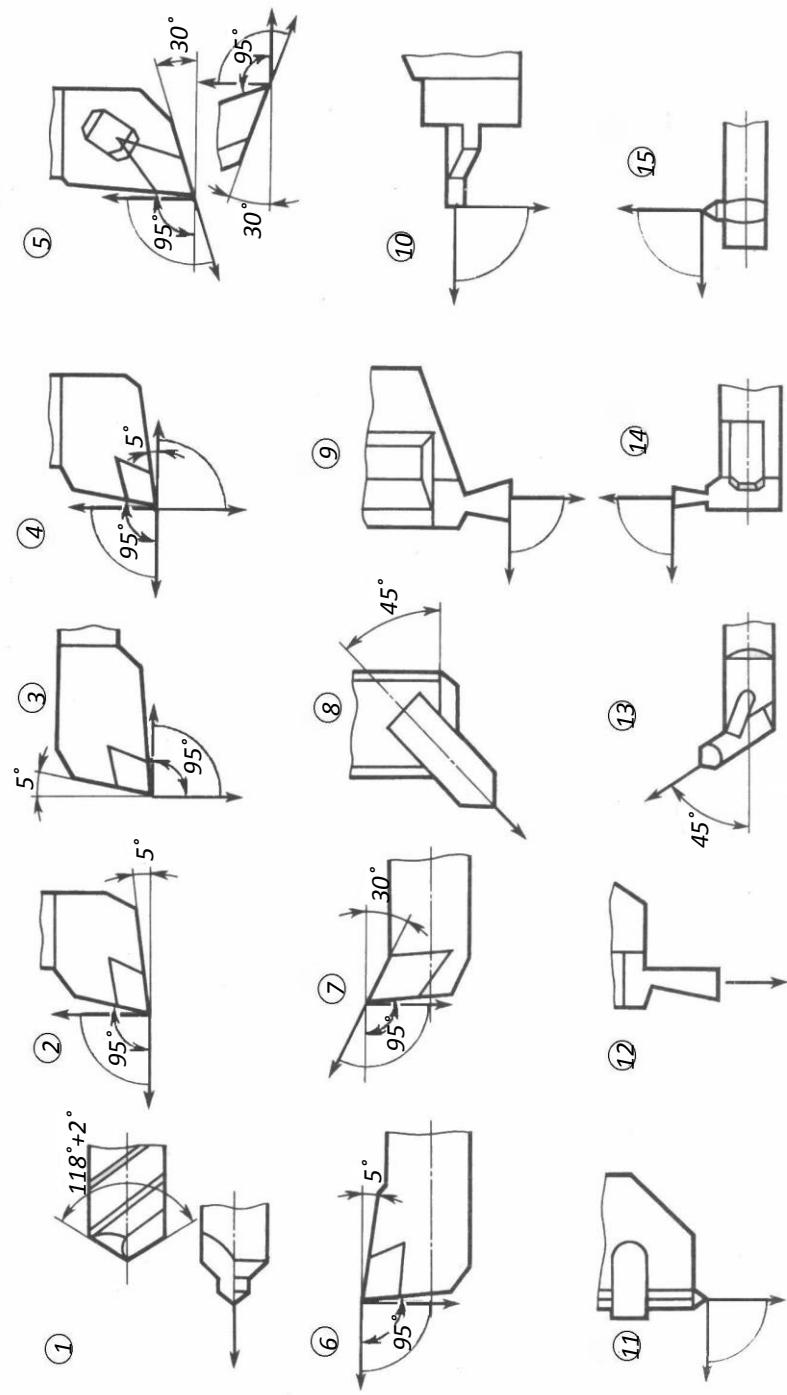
Номенклатура різальних інструментів для токарних верстатів з ЧПУ із вказанням напрямів робочої подачі:
